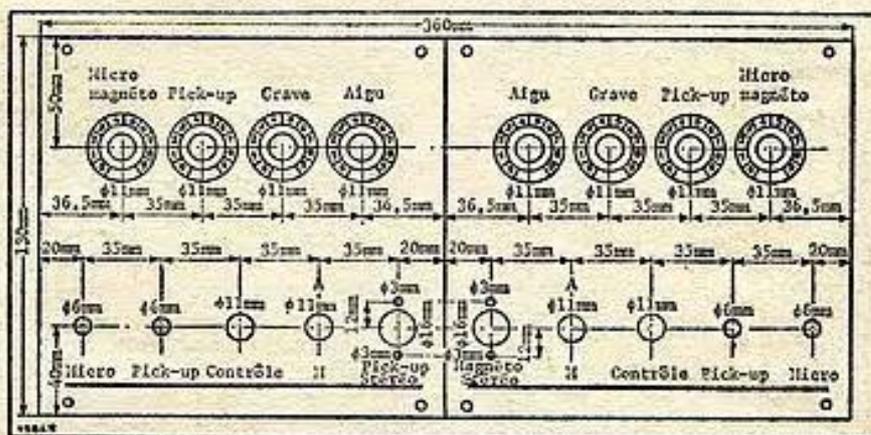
Dimensions et cotes de perçage de la plaque arrière.
